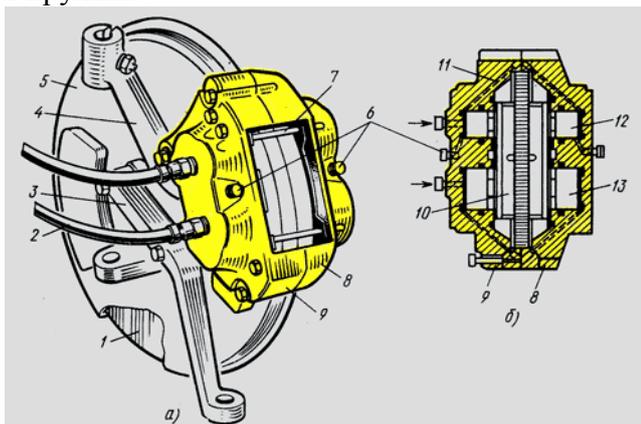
Колесный дисковый тормозной механизм с гидроприводом: а – в сборе, б - разрез по оси колесных тормозных цилиндров
